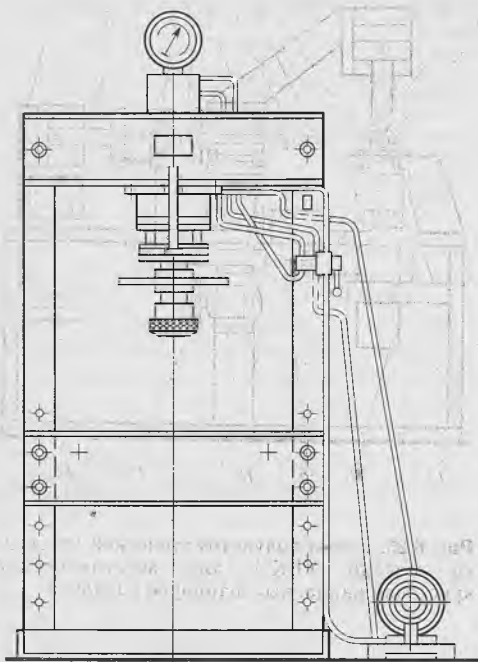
Универсальный гидравлический пресс модели 2135-1
